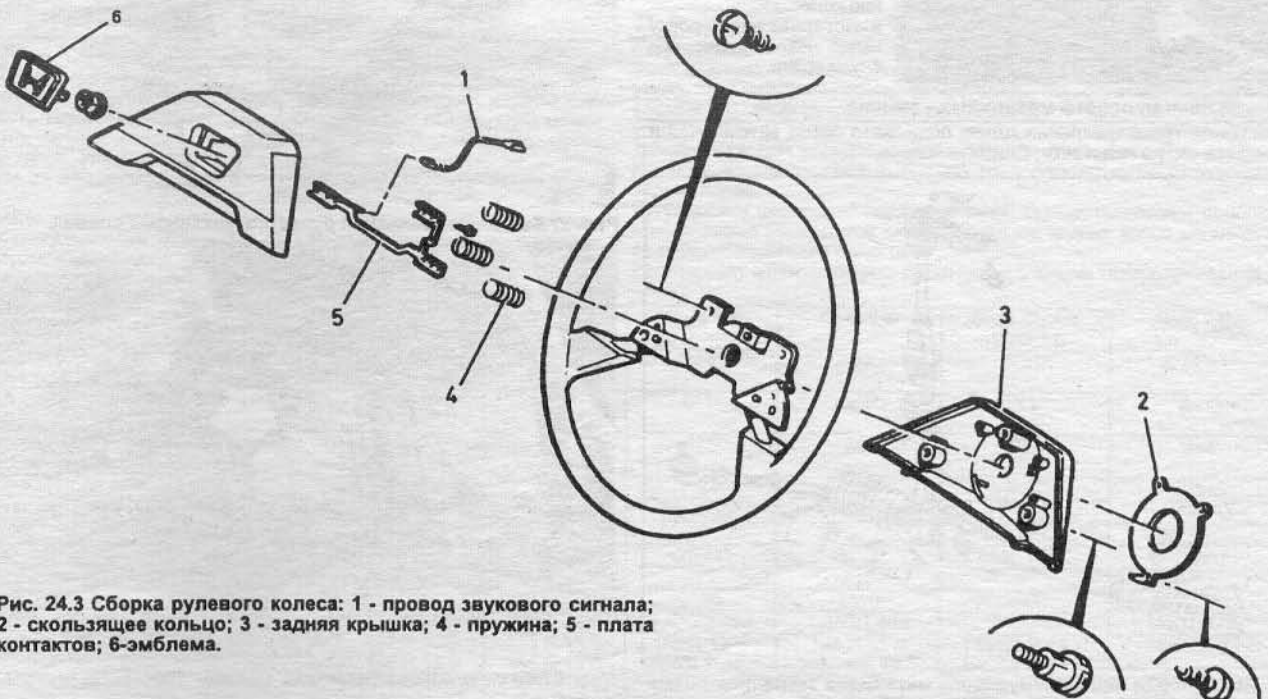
Сборка рулевого колеса: 1 - провод звукового сигнала; 2 - скользящее кольцо; 3 - задняя крышка; 4 - пружина; 5 - плата контактов; 6 - эмблема.
